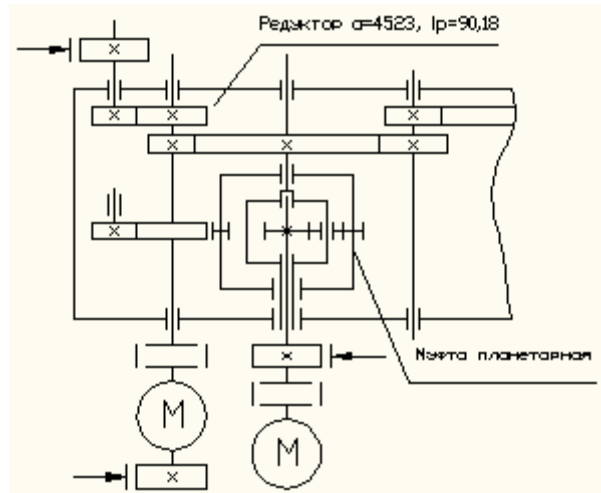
Редуктор механизма подъема с встроенной планетарной муфтой
